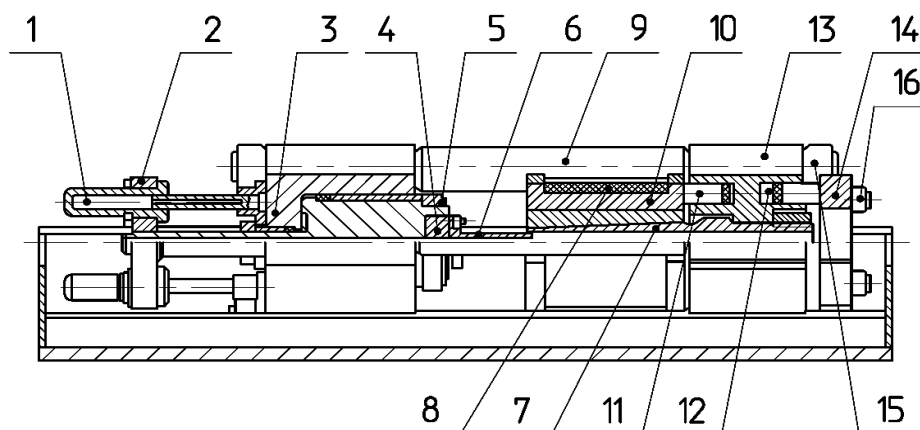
Схема пресса для прессования из заготовки технологически неограниченной длины:
